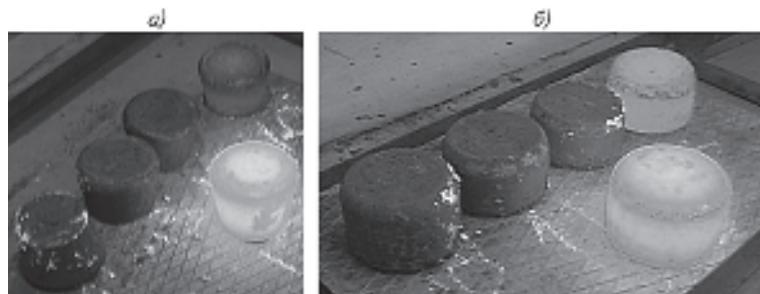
Внешний вид заготовок на разных стадиях ковочного передела:
